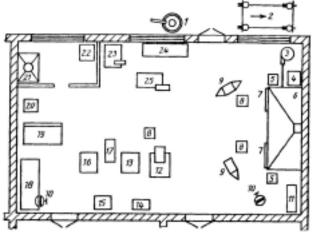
Размещение оборудования в типовой сельской кузнице: 1— устройство для ошиновки колес; 2— ставок для ковки лошадей; 3— вентилятор; 4— ящик с углем; 5— бачки с водой: 6— кузнечный горн на два огня; 7— вешалки для инструмента; 8— столики для инструмента; 9— наковальни; 10— стуловые тиски; 11— пирамида для кузнечного инструмента; 12— пневматический молот; 13— печь для нагрева заготовок; 14— бак с мазутом; 15— воздуходувка для печей; 16— печь для нагрева поковок и деталей при термической обработке; 17— бак с закалочной жидкостью; 18— слесарный верстак; 19— правильная плита; 20— переносной кузнечный гори; 21— сварочный стол; 22— электросварочный агрегат; 23— наждачный станок; 24— стеллаж для заготовок; 25— ножницы
